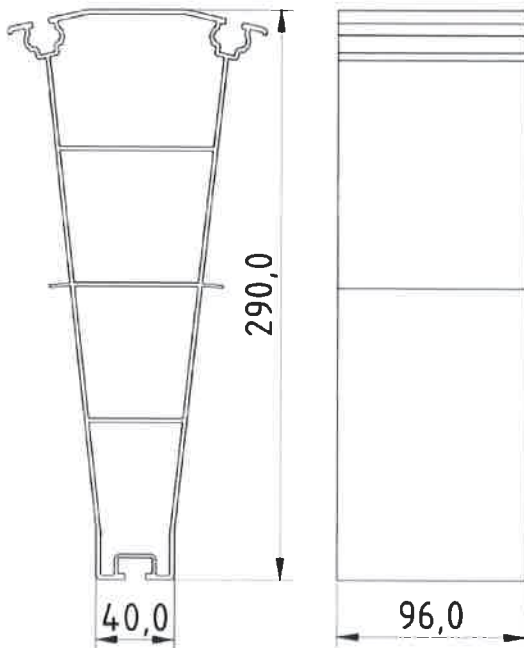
FixZ-15 Systemprofil Mitte 96 mm
